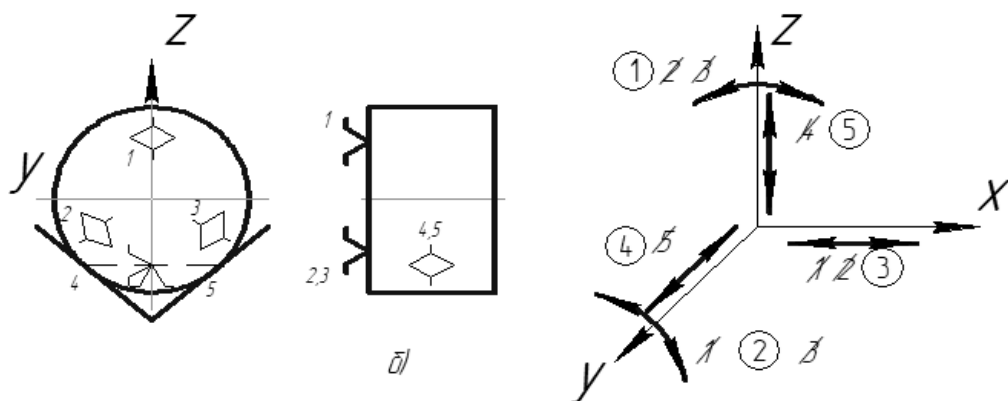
Базування циліндричної заготовки у призмі з упором у п'яту
